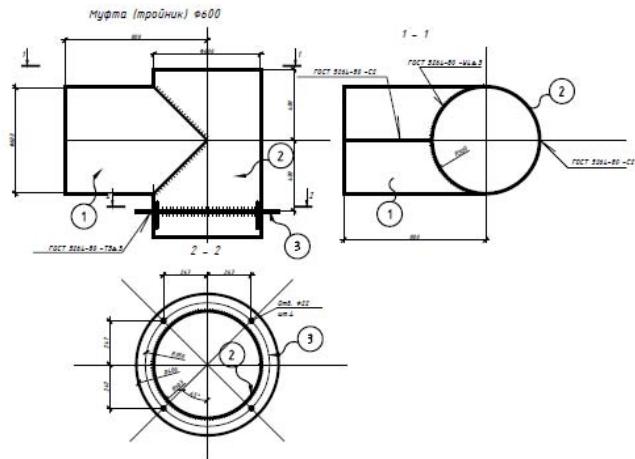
Опорный тройник для соединения труб Фуранфлекс и газоотводящей трубы
